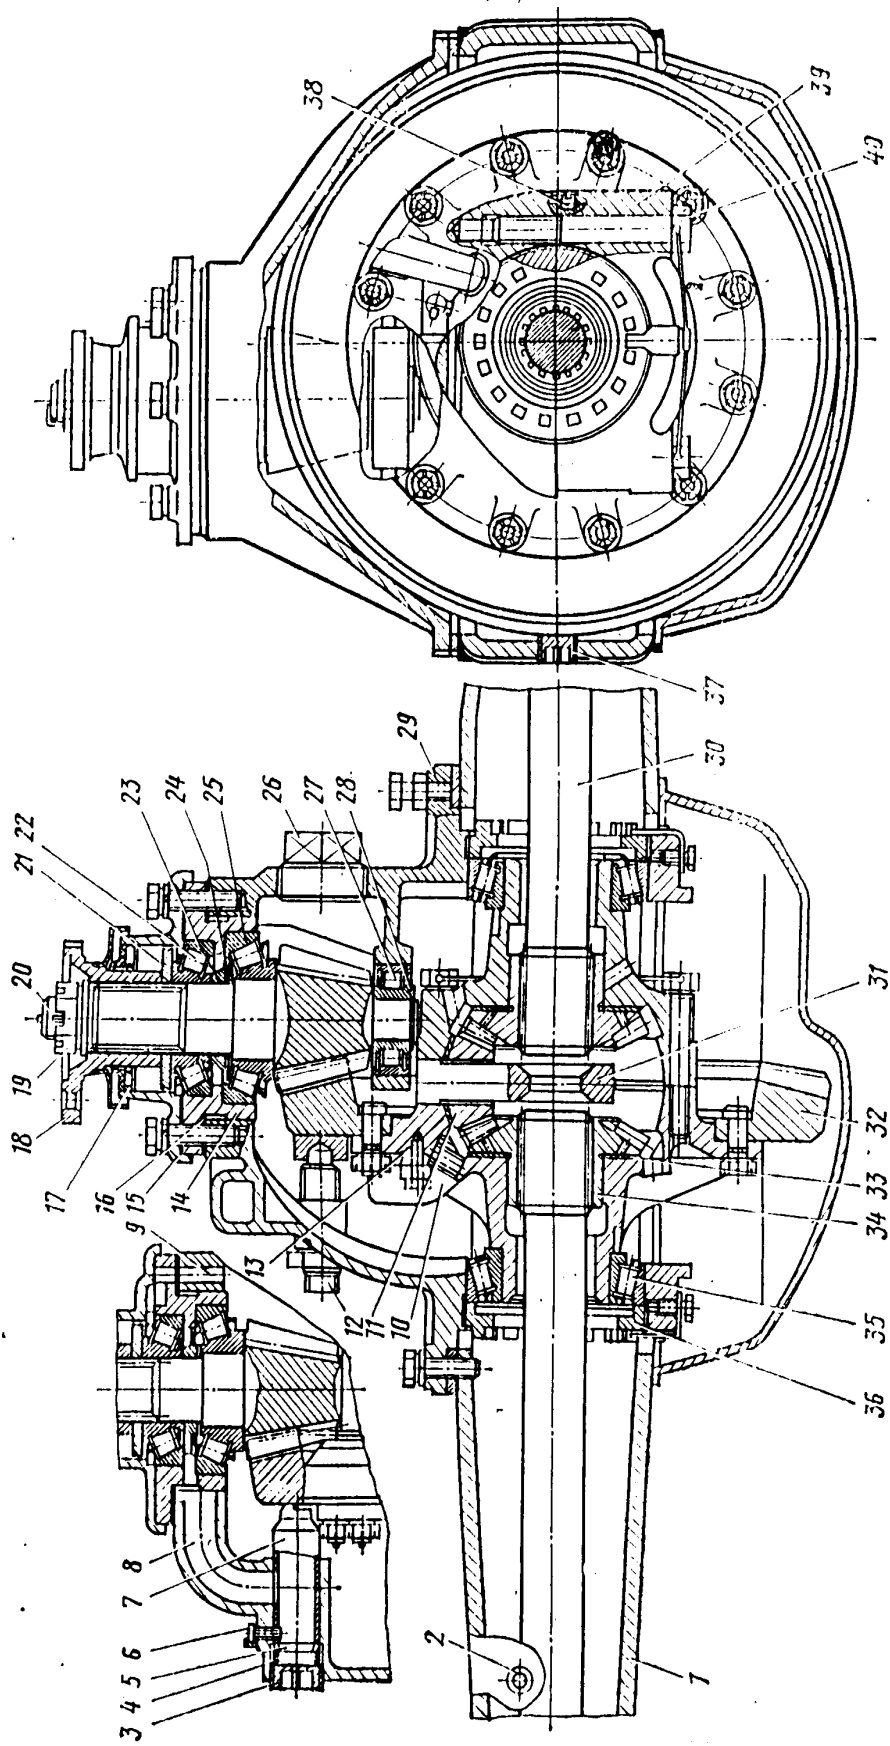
Главная передача автомобиля ГАЗ-53: 1 – картер заднего моста; 2 – сапун; 3 и 26 – пробки; 4 – пружина; 5 – тарелка; 6 и 40 – болты; 7 – маслосъемная трубка; 8 – и 9 – каналы; 10 – маслоулавливатель; 11 – сателлит; 12 – винт упора; 13 – опорная шайба сателлитов; 14 – муфта подшипников; 15 и 39 – крышки; 16 и 24 – регулировочные прокладки; 17 – сальник; 18 – фланец; 19 – корончатая гайка; 20 – ведущая шестерня; 21 – маслостонное кольцо; 22, 25 и 35 – конические роликоподшипники; 23 – распорное кольцо; 27 – цилиндрический роликоподшипник; 28 – стопорное кольцо; 29 – картер редуктора; 30 – полуось; 31 – крестовина; 32 – ведомая шестерня; 33 – опорная шайба шестерни полуоси; 34 – шестерня полуоси; 35 – регулировочная гайка; 37 – маслосливная пробка; 38 – установочный штифт
